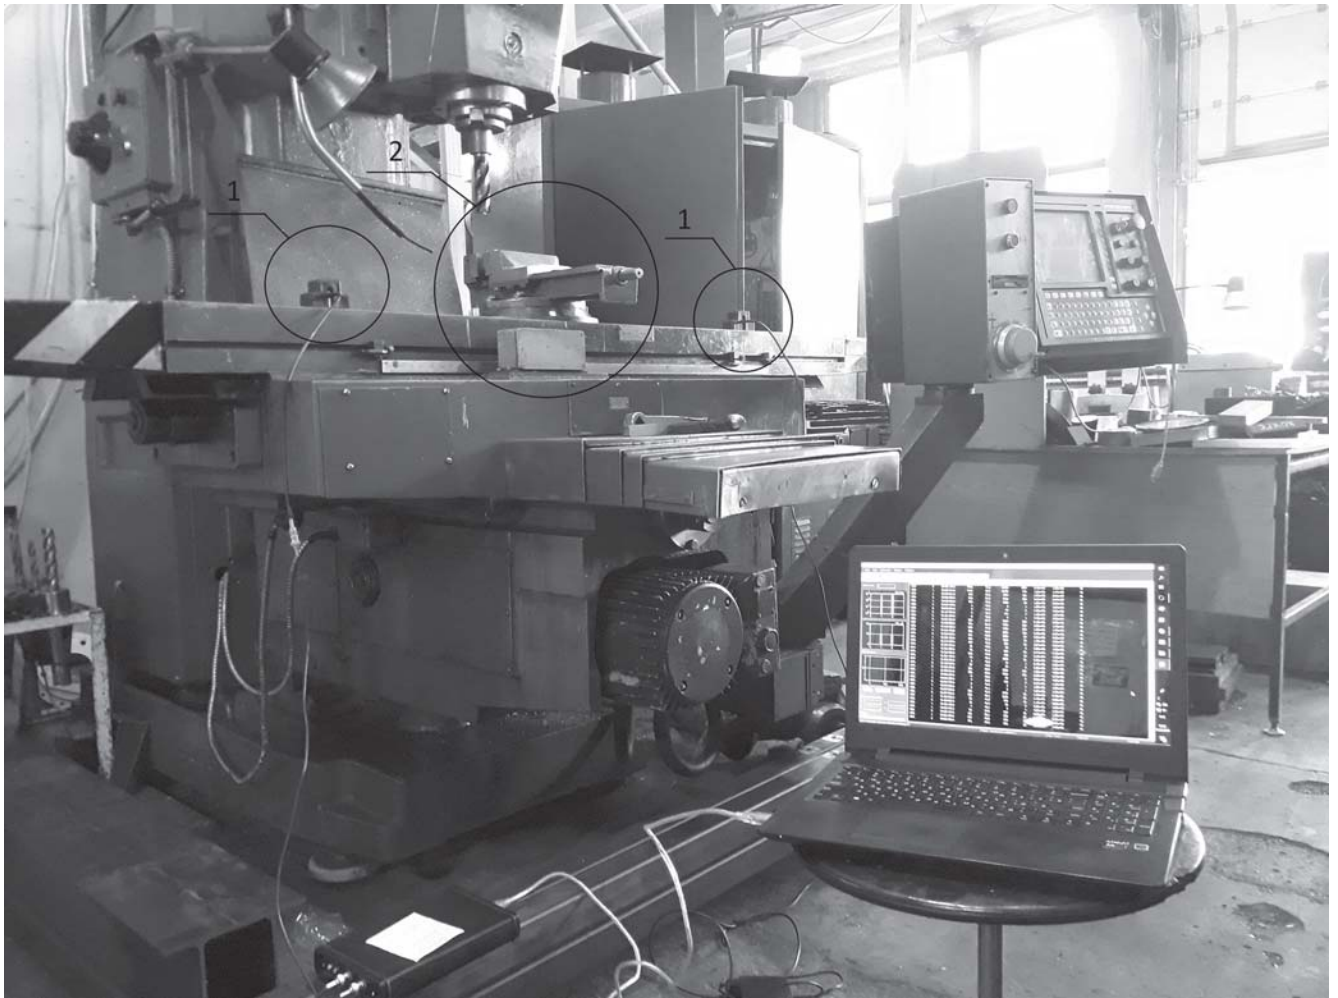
Фрезерный станок с ЧПУ (общий вид, защитный кожух снят): 1 — стол станка; 2 — тиски
